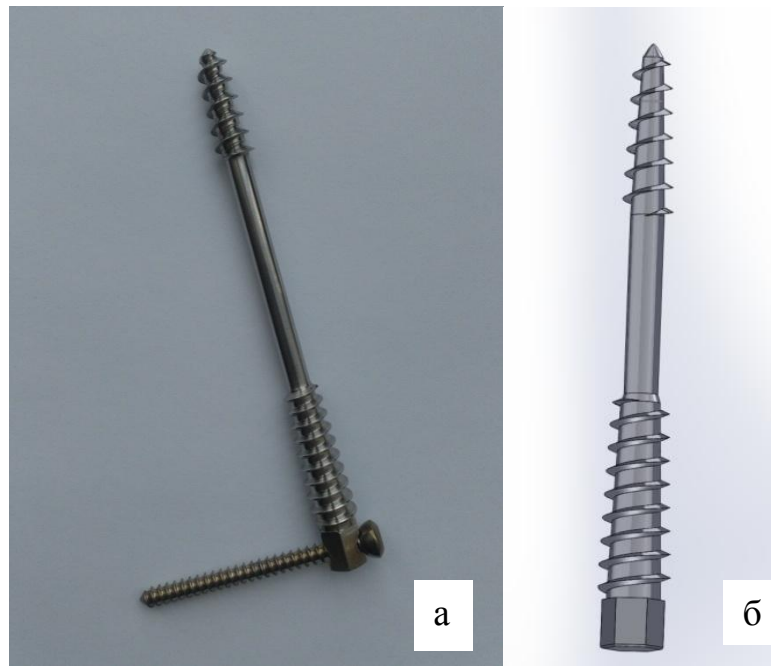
а) винт с двойной разношаговой резьбой в собранном виде (патент РФ №38579); б) компьютерная модель металлоконструкции
